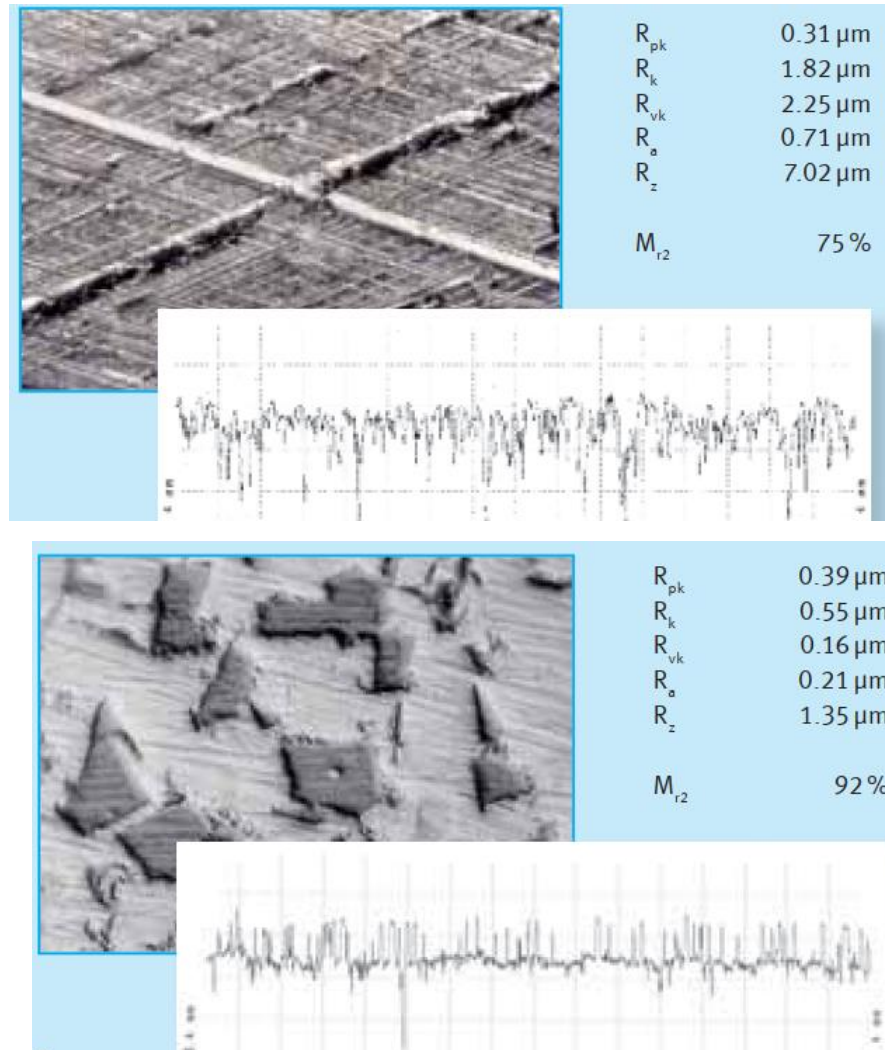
Поверхня циліндра з сірого чавуну після фінішної обробки.
